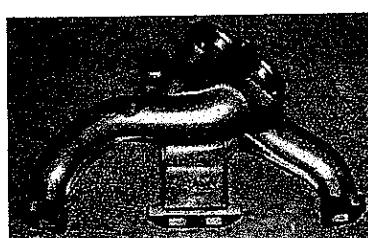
Exhause & Intake Manifold 7K EFI
